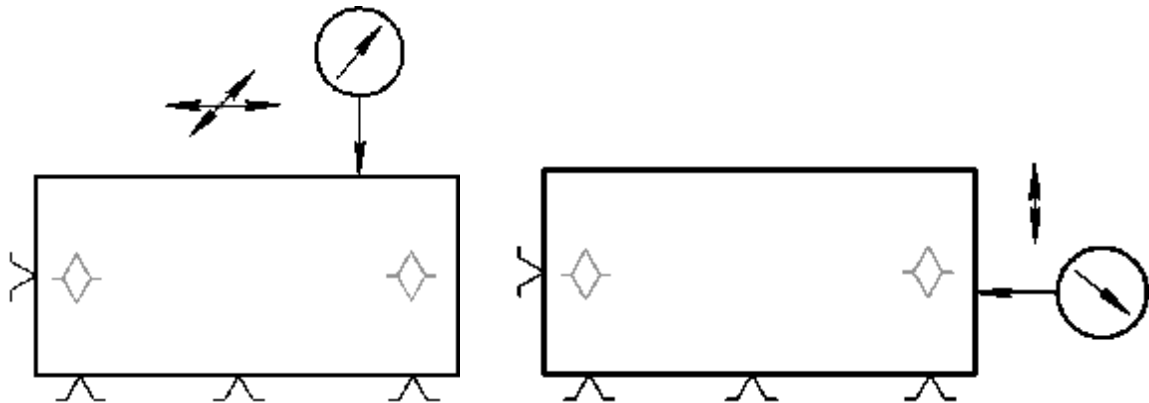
Схеми контролю плоских поверхонь деталей та їх базування
